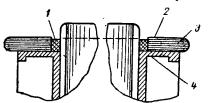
Цилиндрический обмоткодержатель, прилегающий к активной стали якоря или ротора:
